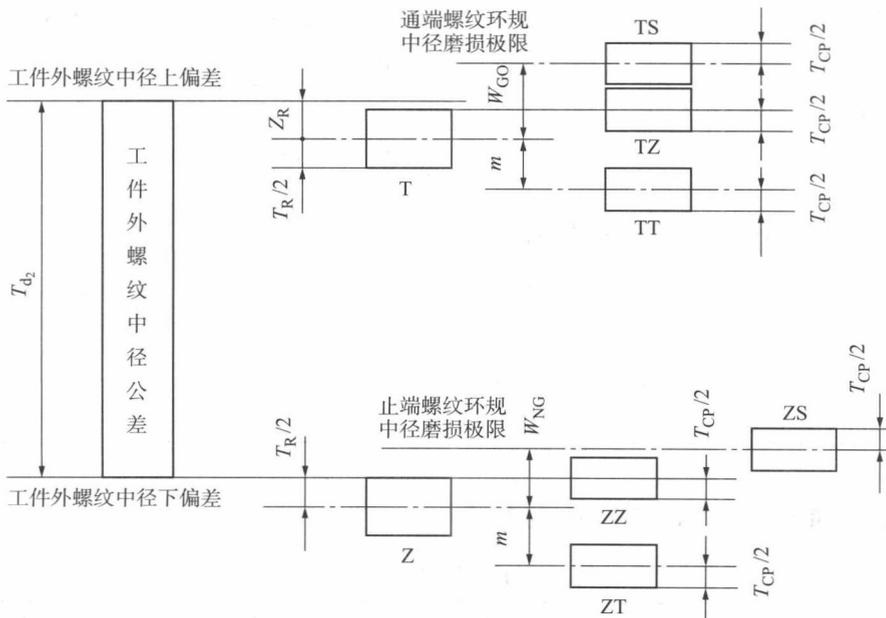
检验工件外螺纹用的螺纹量规中径公差带
